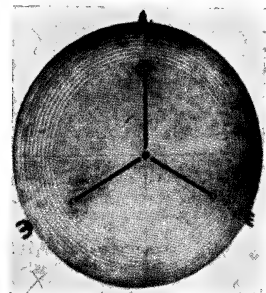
Шайба для деления заготовок при нарезании зубчатых колес. 1564 г. Фотография с натуры проф. Фельдхауза.
